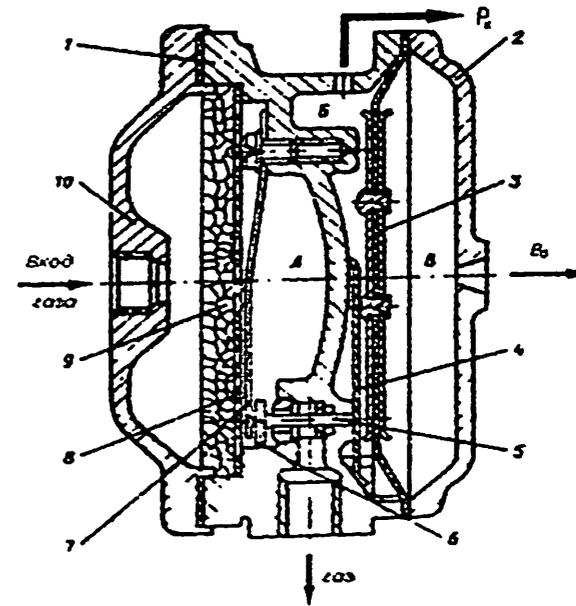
Вакуумный включатель-фильтр мод. VFF—30; 1 - корпус; 2 - крышка; 3 - диафрагма; 4 - нажимной рычаг; 5 - шток клапана; 6 - тарельчатый клапан; 7 - пластинчатая пружина; 8 - металлическая сетка; 9 - пластинчатый фетровый фильтр; 10 - крышка
